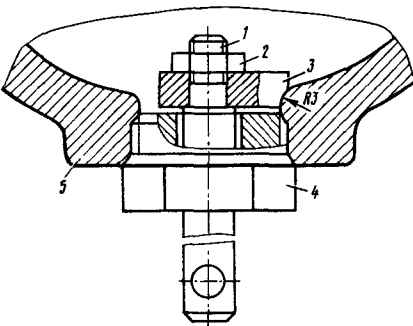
Приспособление для скругления внутренней кромки адаптерного отверстия втулки цилиндра дизелей типа Д100: 1 — стержень; 2 — гайка; 3 — резец; 4 — пробка; 5 — втулка цилиндра
